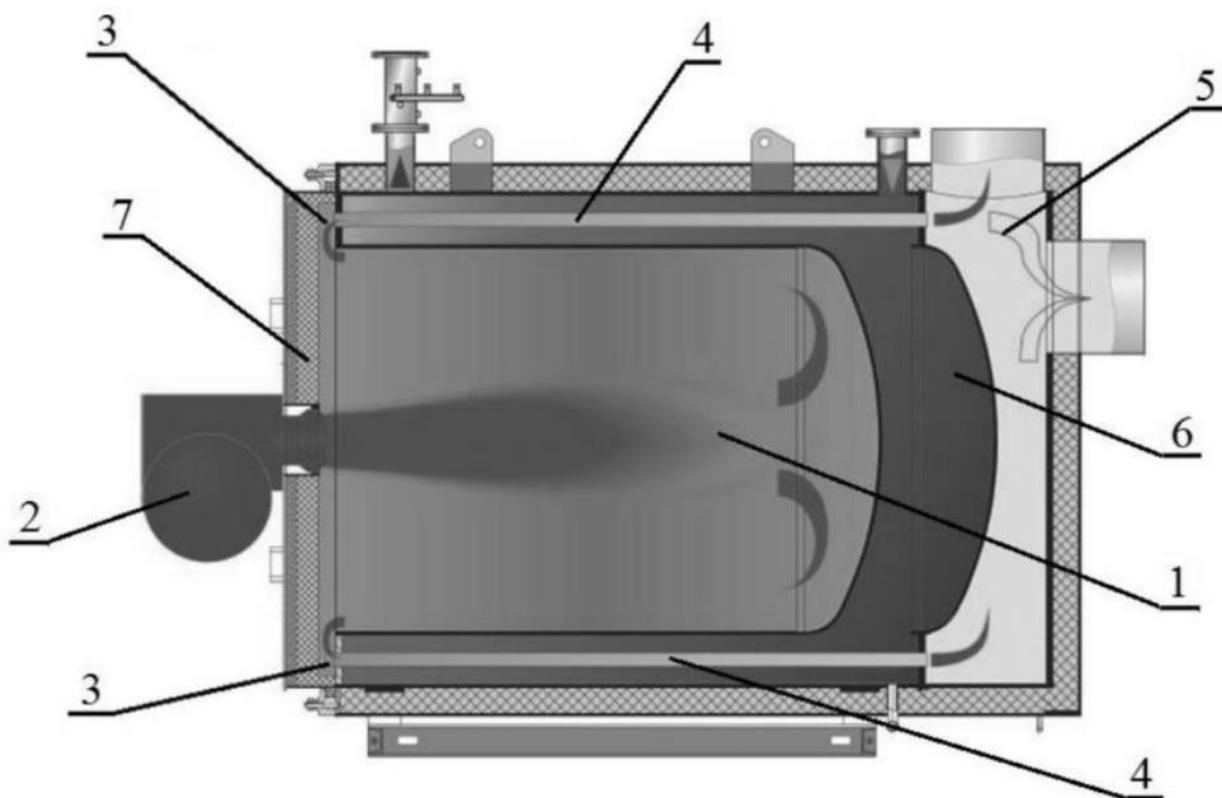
Конструктивная схема жаротрубного котла [31]: 1 – жаровая труба; 2 – горелка; 3 – поворотная камера; 4 – конвективный пучок дымогарных труб; 5 – сборный дымовой короб; 6 – водяной объем; 7 – крышка.
